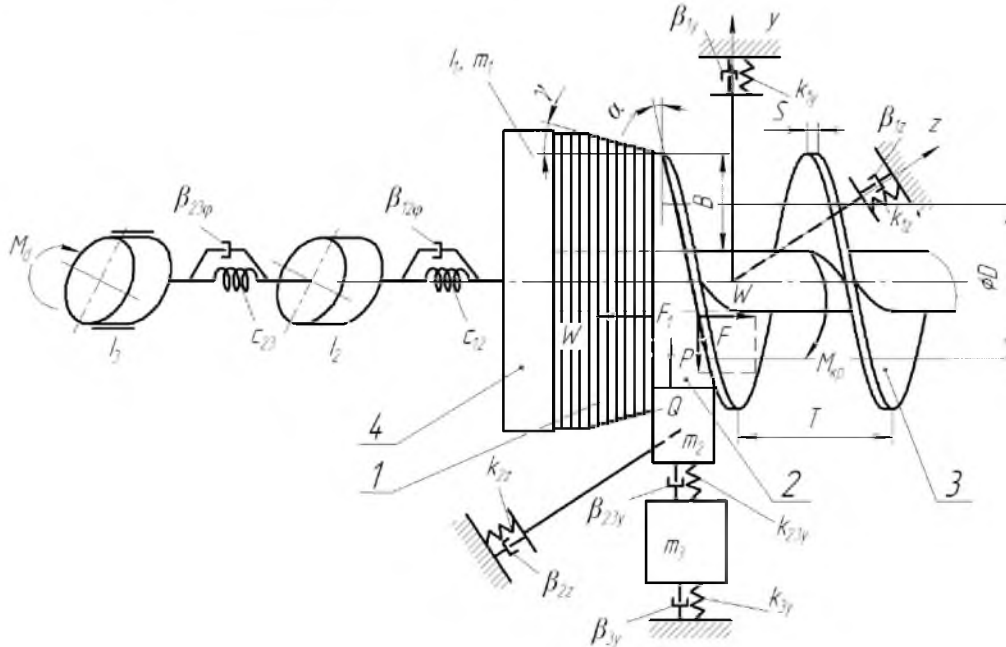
Розрахункова схема процесу калібрування витка конічної гвинтової заготовки на крок:
